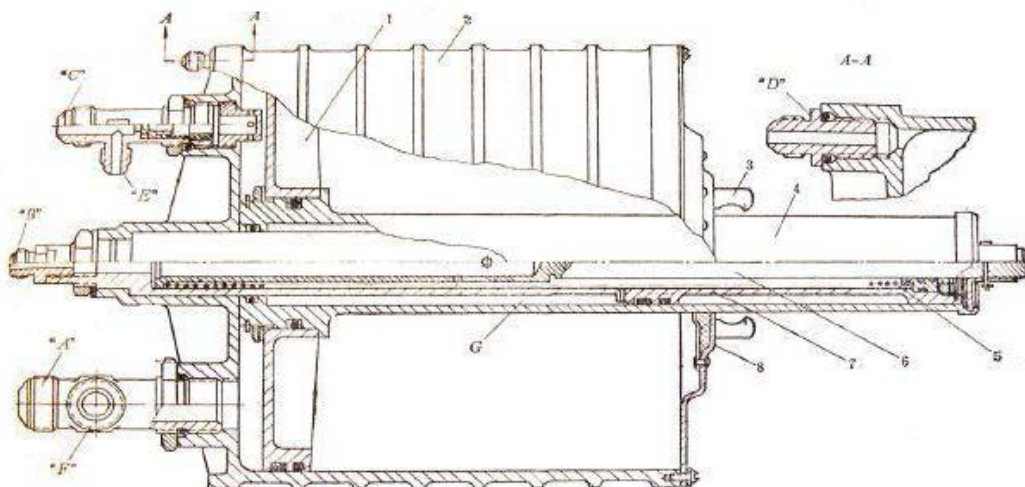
Конструктивная схема гидробака закрытого типа [4].
